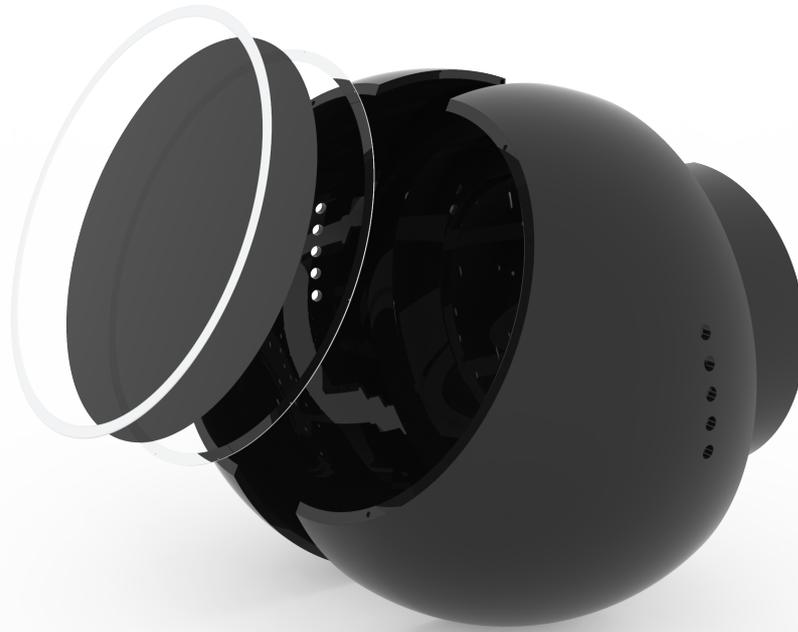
Render 5 de ACCOM One explosionado con todas las piezas de las que se compone
